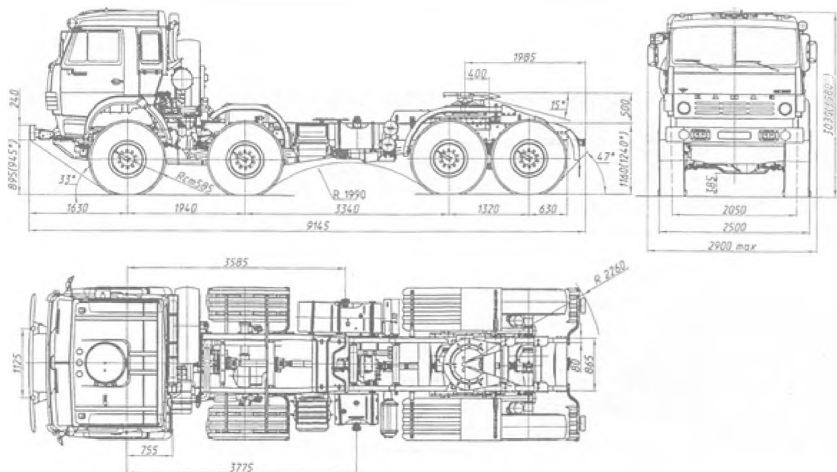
Автомобиль-тягач седельный КАМАЗ-6450. Габаритные размеры
